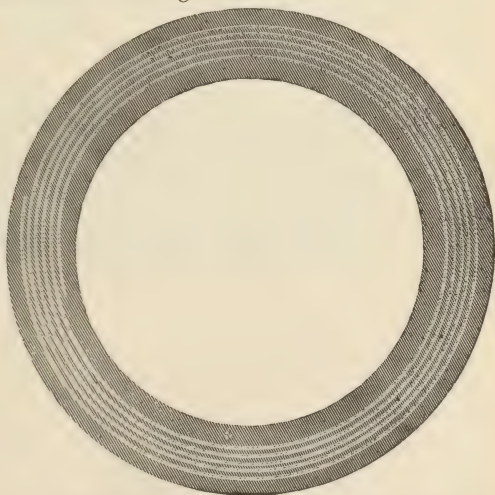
Schlauch mit 46 mm Innendurchmesser, 9 mm Wandstärke, 5 Einlagen
